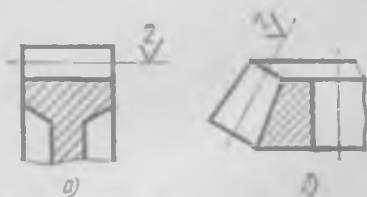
Обозначение шероховатости рабочих поверхностей зубьев
